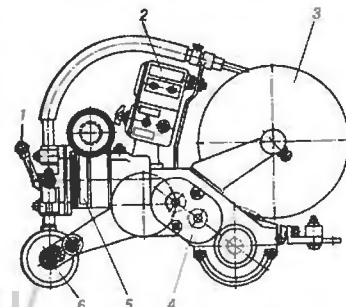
Універсальний зварювальний трактор ТС-42:
